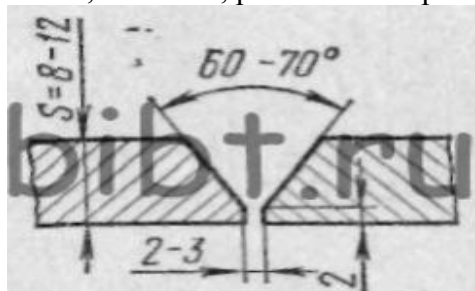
Подготовка кромок труб под сварку при толщине стенок 8-12 мм.
